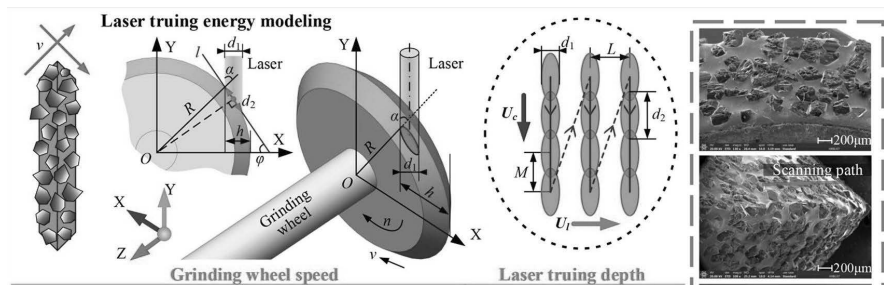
Імпульсний лазерний принцип правки V-подібного крупнозернистого гальванічного CBN шліфувального круга [5]
